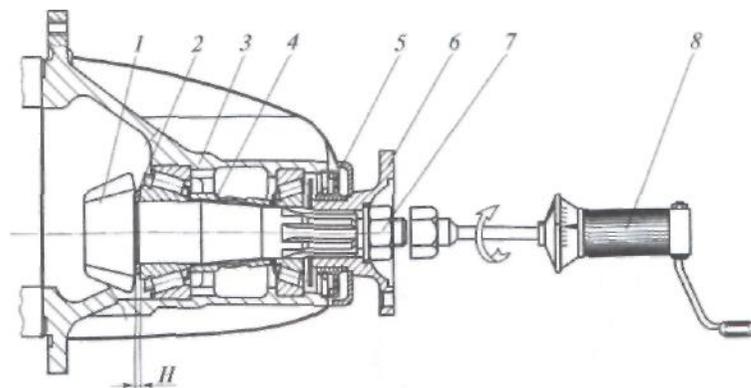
Схема проверки момента проворачивания ведущего колеса (без дифференциала):
